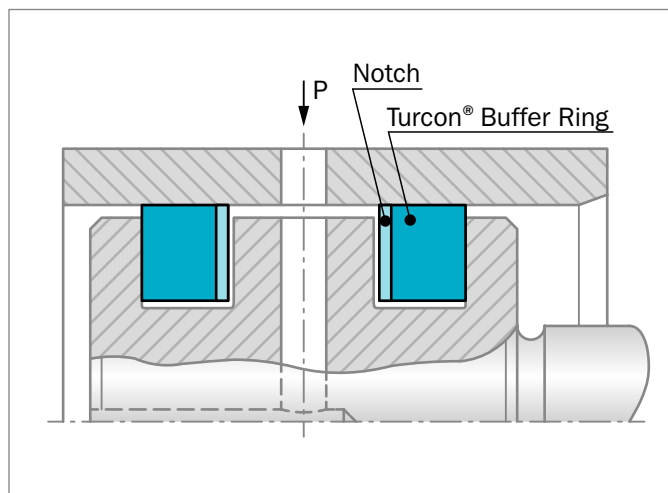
Korrekter Einbau des Turcon® Buffer Rings in einer Bohrung
